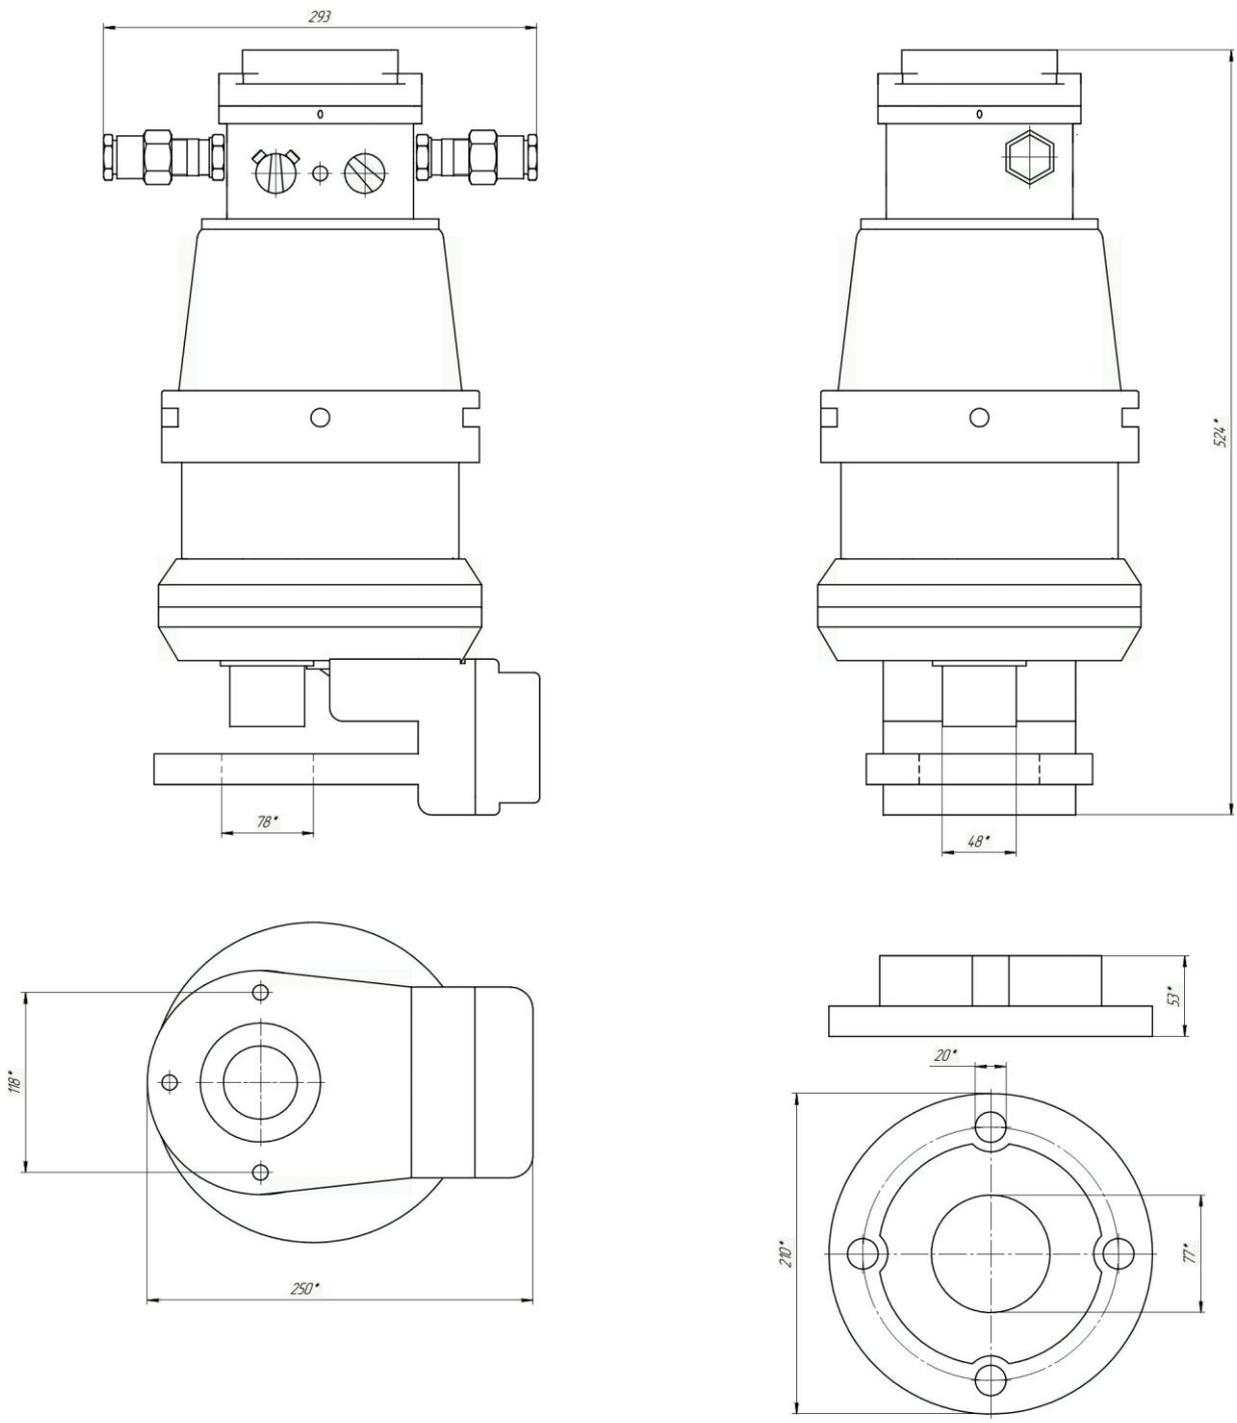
Общий вид электроприводов серии ЭПГТ-1 с максимальными габаритными и установочными размерами
